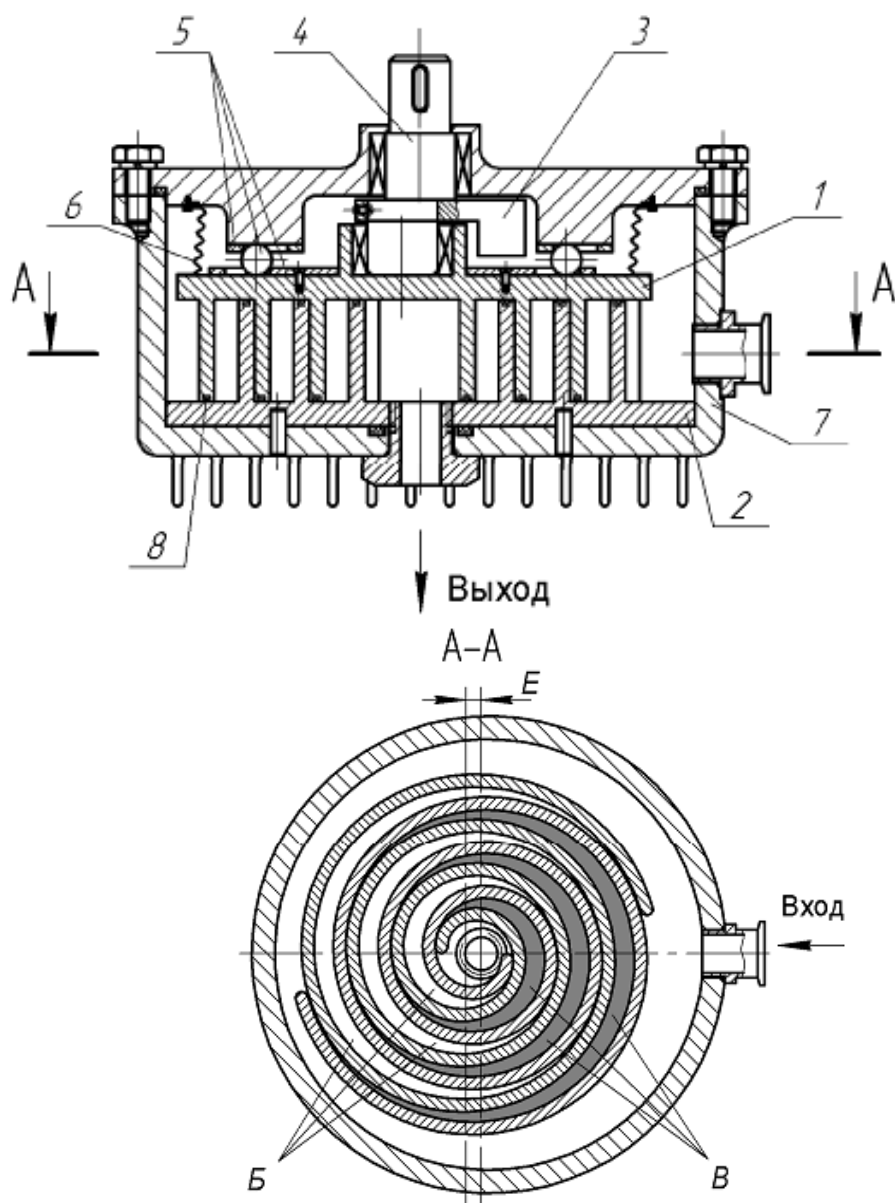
Спиральный вакуумный насос: 1 – подвижная спираль; 2 – неподвижная спираль; 3 – противовес; 4 – эксцентриковый вал; 5 – противоповоротное устройство; 6 – сильфон; 7 – корпус; 8 – уплотнитель
